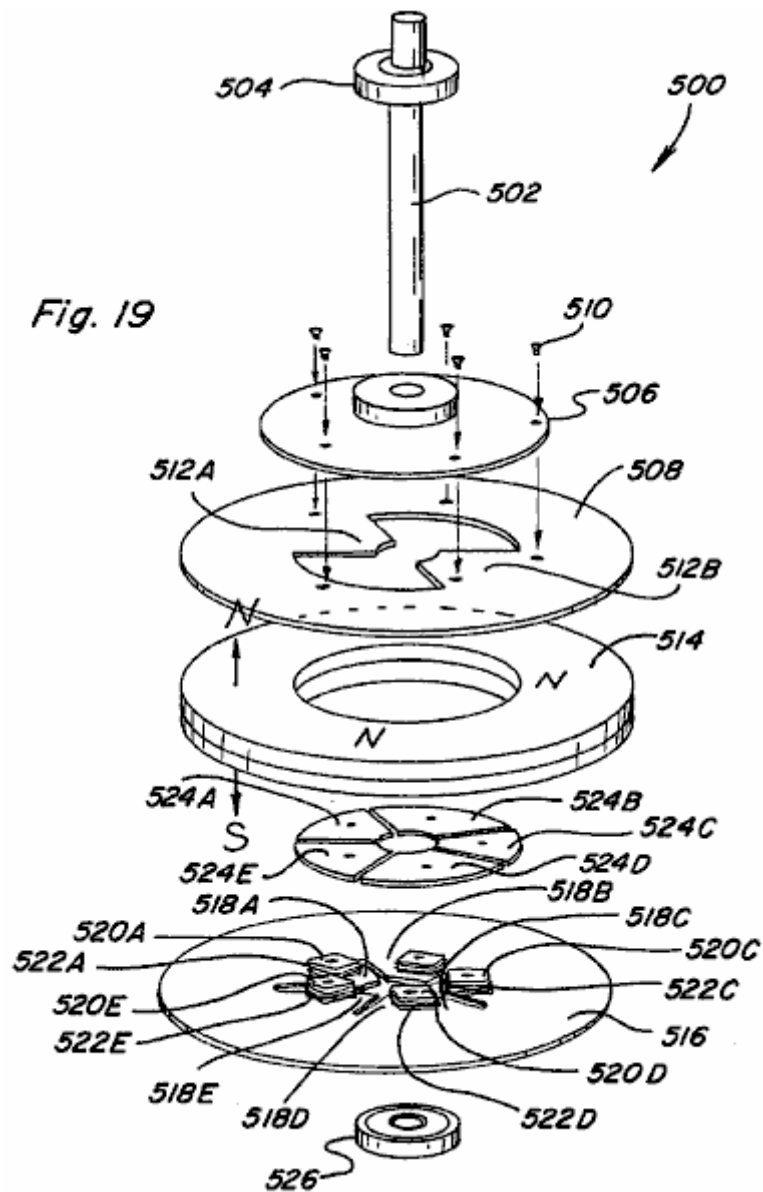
est une vue en perspective éclatée d'un appareil à mouvement rotatif ;
